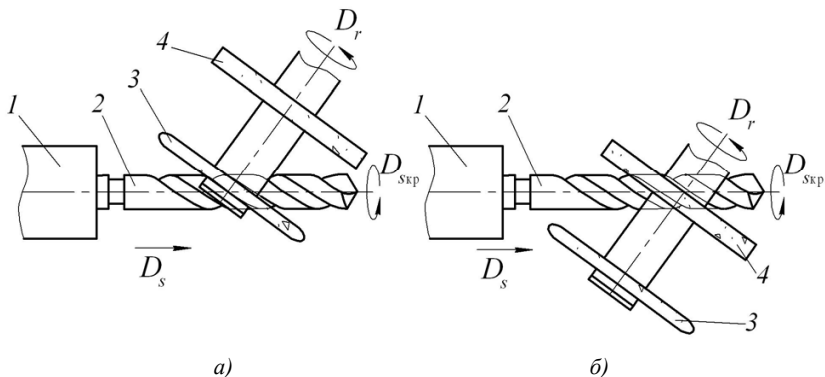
Последовательная схема вышлифовывания канавок и спинок сверла: а) обработка канавки; б) обработка спинки: 1 – цанговый патрон; 2 – заготовка; 3 – канавочный круг; 4 – спиночный круг
